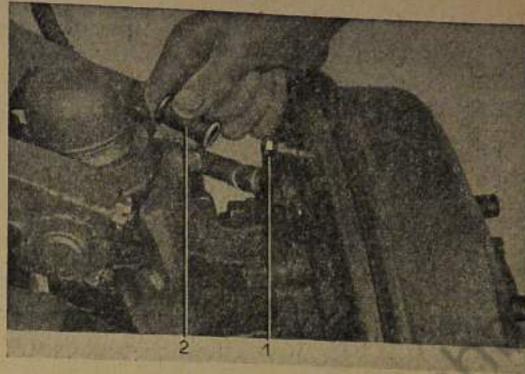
Verschlußschraube für Entlüftungsventil heraus-schrauben
